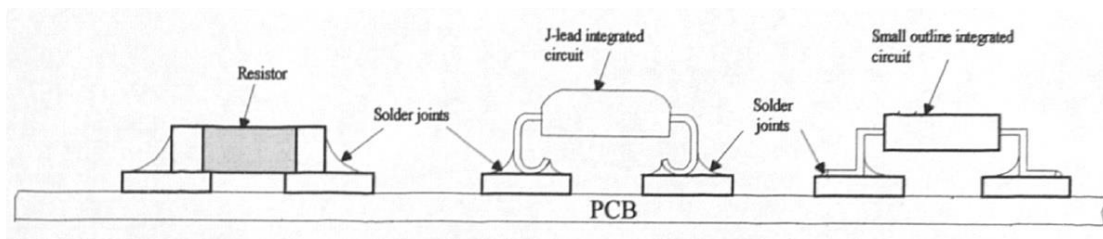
Juntas de soldadura da tecnologia SMT in “Hui, *Analysis of surface mount technology solder joints*, 1996”
